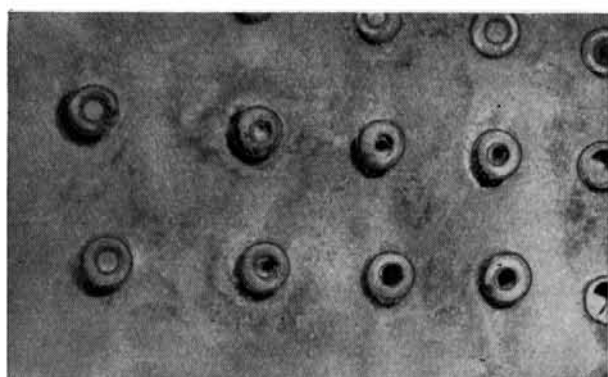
Abzehrung einer kupfernen Feuerbüchse durch Schwefeldioxyd
